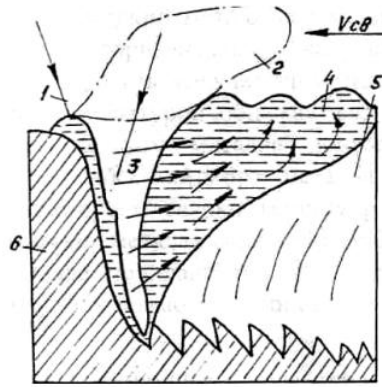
Схема формирования сварного соединения при лазерной сварке с глубоким проплавлением: 1 – лазерное излучение, 2 – плазменный факел, 3 – парогазовый канал, 4 – хвостовая часть сварочной ванны, 5 – закристаллизовавшийся металл шва, 6 – свариваемый металл
